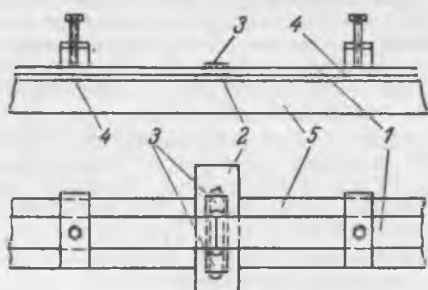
Стык шин, подготовленных к сварке.
